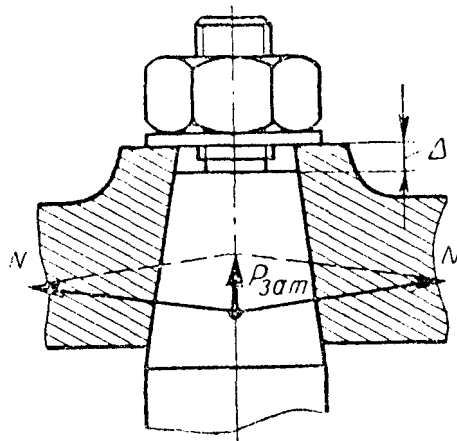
Затяжка конусного з'єднання гайкою
